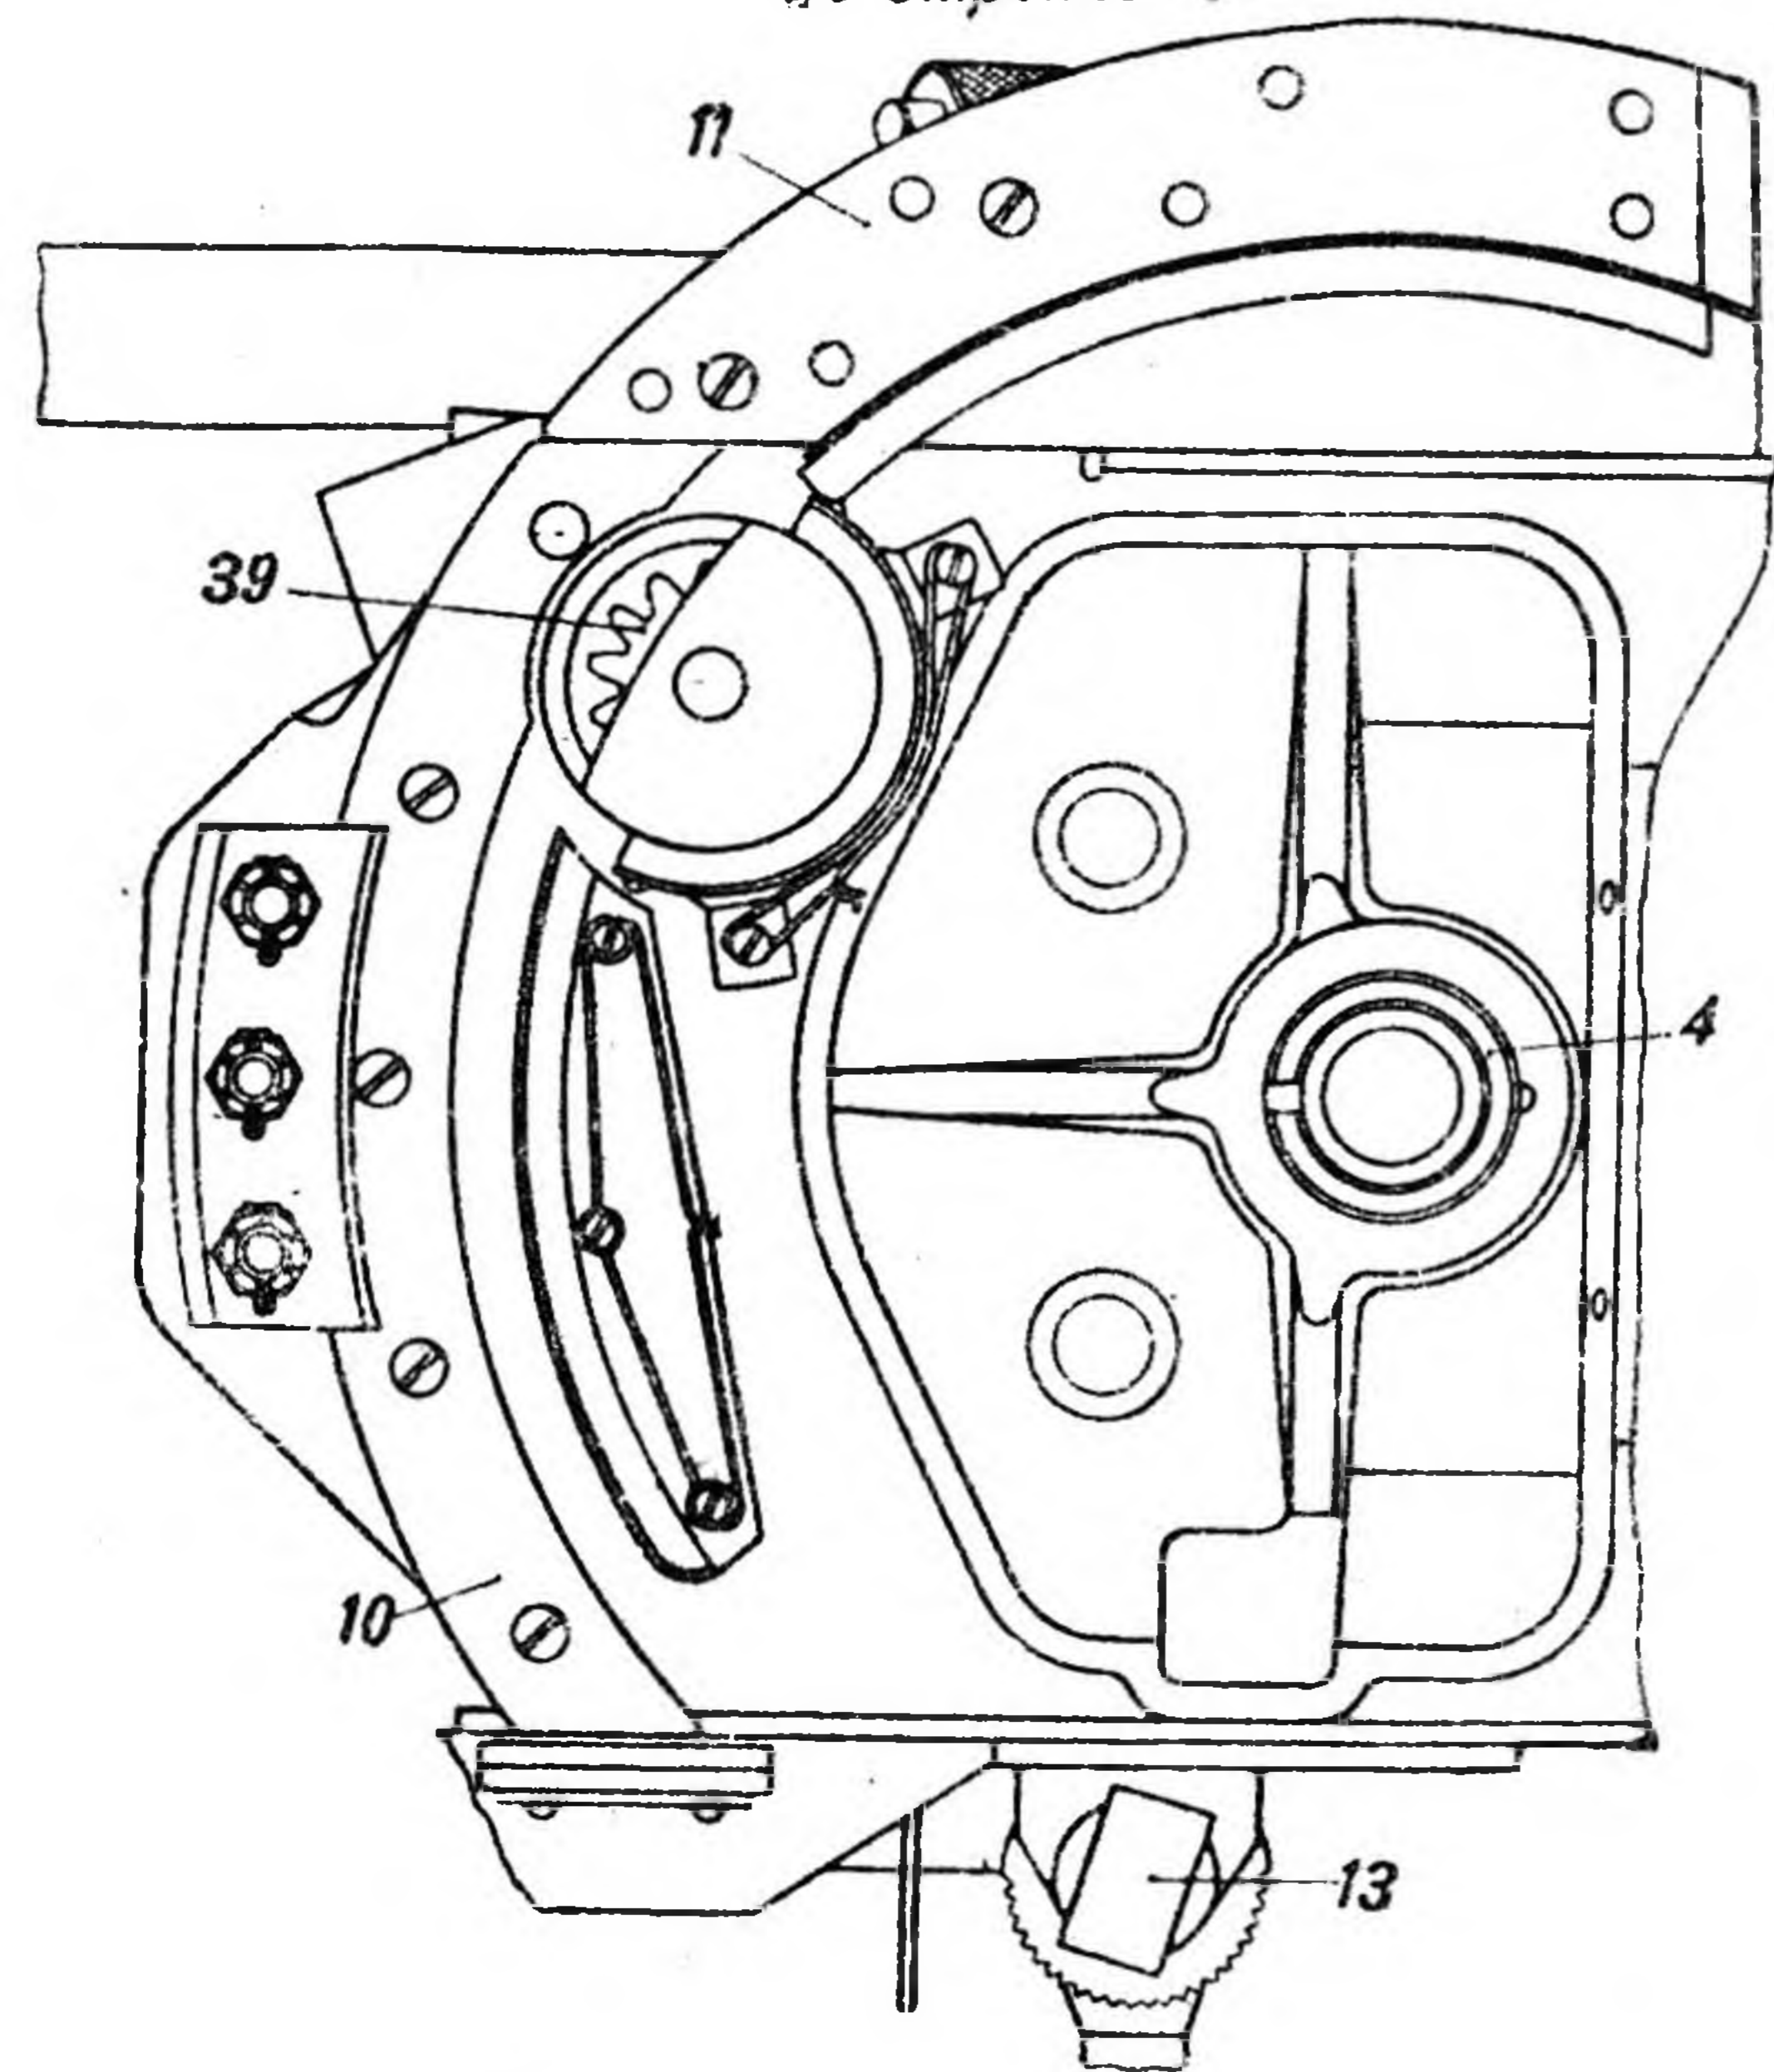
Верхний станок (вид сверху и вид снизу) и подъемный механизм (разрез)
